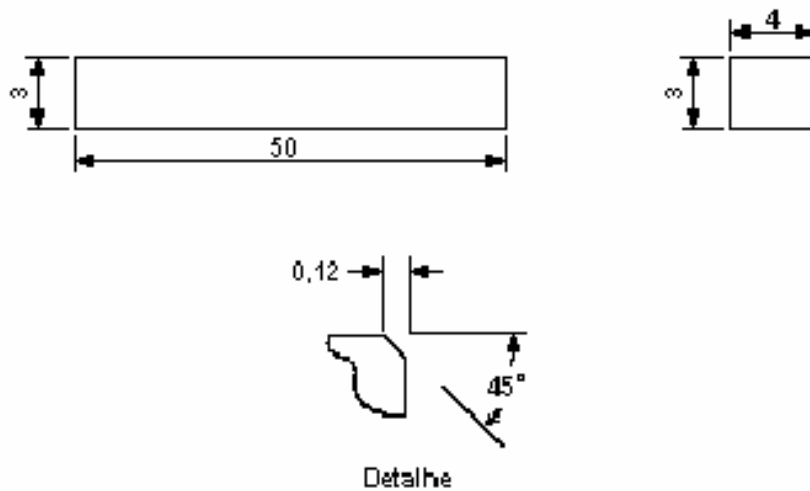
Geometria do CP para Ensaio de Flexão a 4 Pontos (Unidades em mm)
